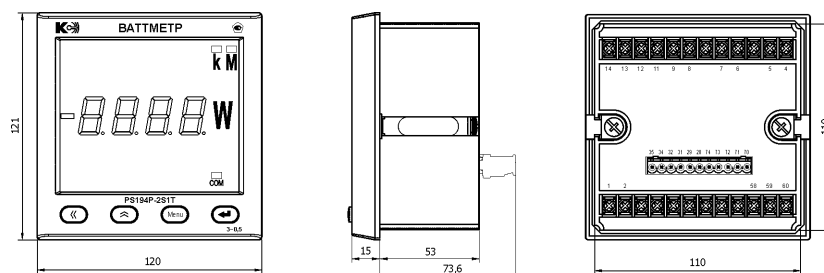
Внешний вид и размеры ваттметра PS194P-2K1T-11001
